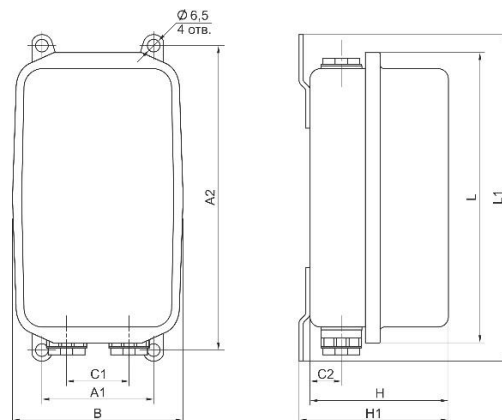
Пускатель ПМ12 100-180А в защитном корпусе. Степень защиты - IP54
